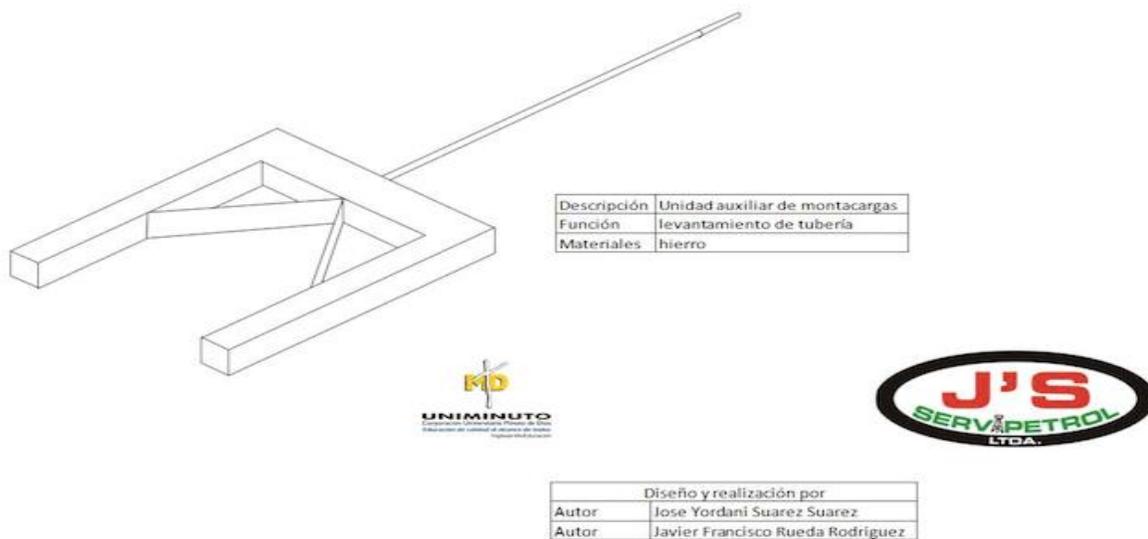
VISTA EN 3D (ISOMETRICO). Fuente: Autoría propia
